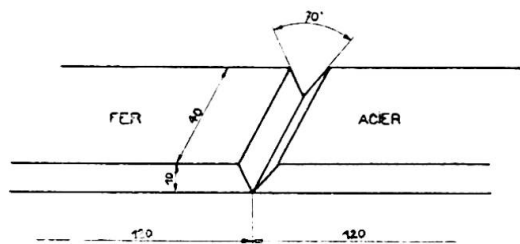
Forme et dimensions de l'éprouvette de pliage.
